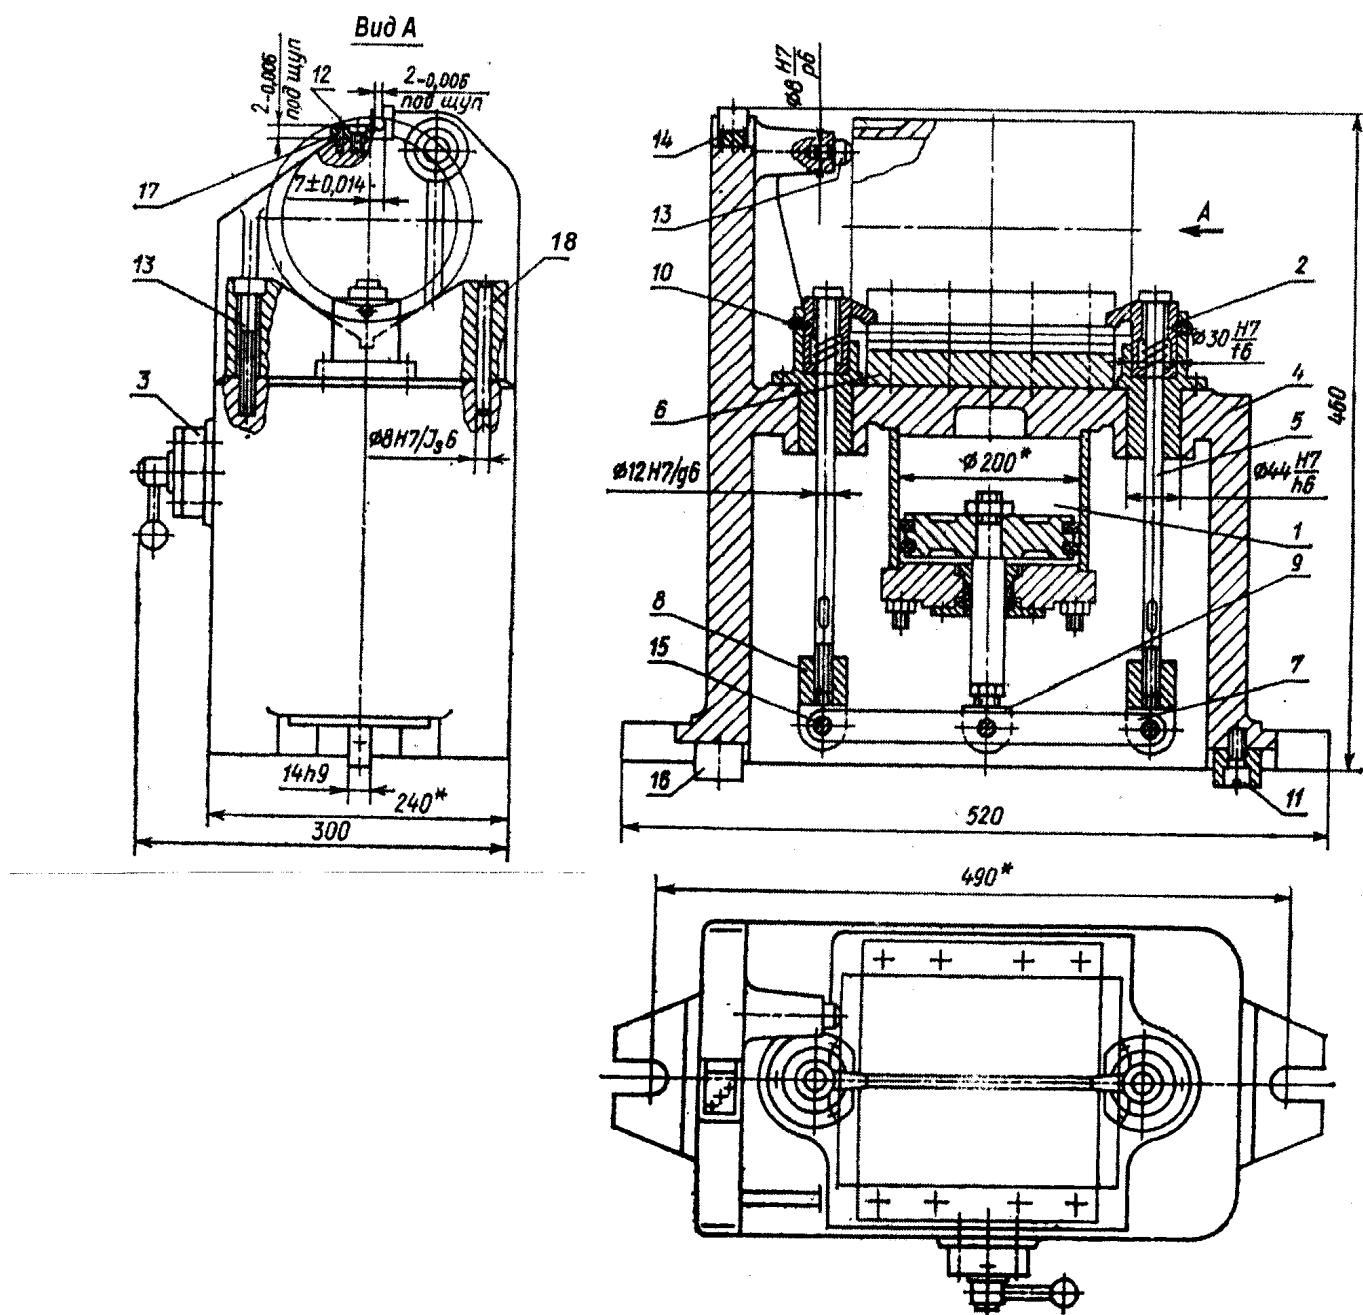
Общий вид приспособления для фрезерования паза
